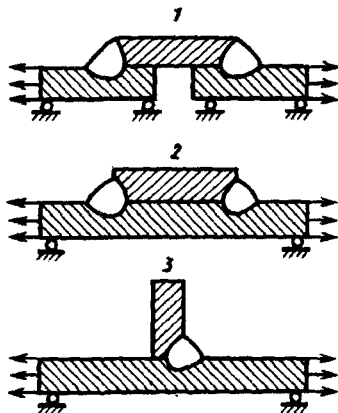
Типовые схемы нагружения сварных соединений с угловыми швами
